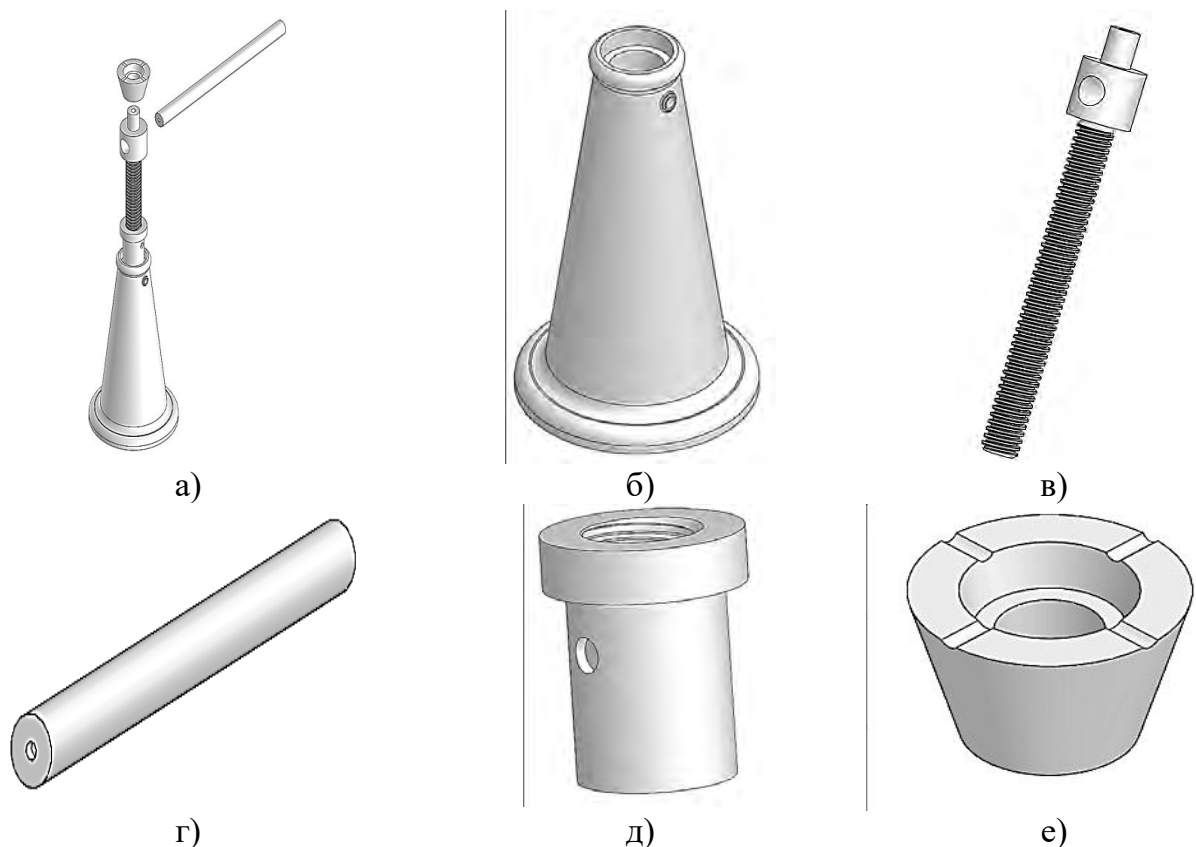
Детали бутылочного домкрата в Компас-3D: а) общий сборочный чертёж домкрата; б) конусообразный корпус; в) винт с трапецидальной резьбой; г) рукоятка; д) втулка с трапецидальной резьбой; е) чашка
